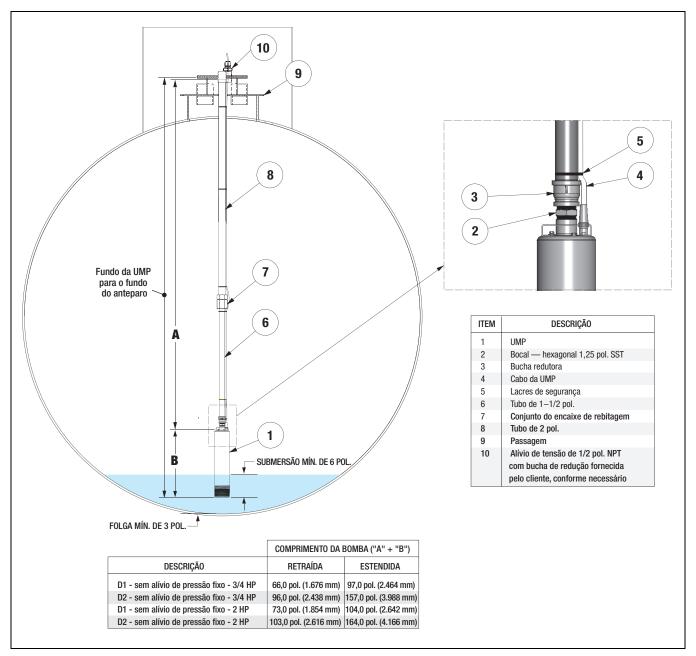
Dimensões da bomba submersível de ARLA/instalação do tanque com montagem de alívio de pressão de bypass ajustável
